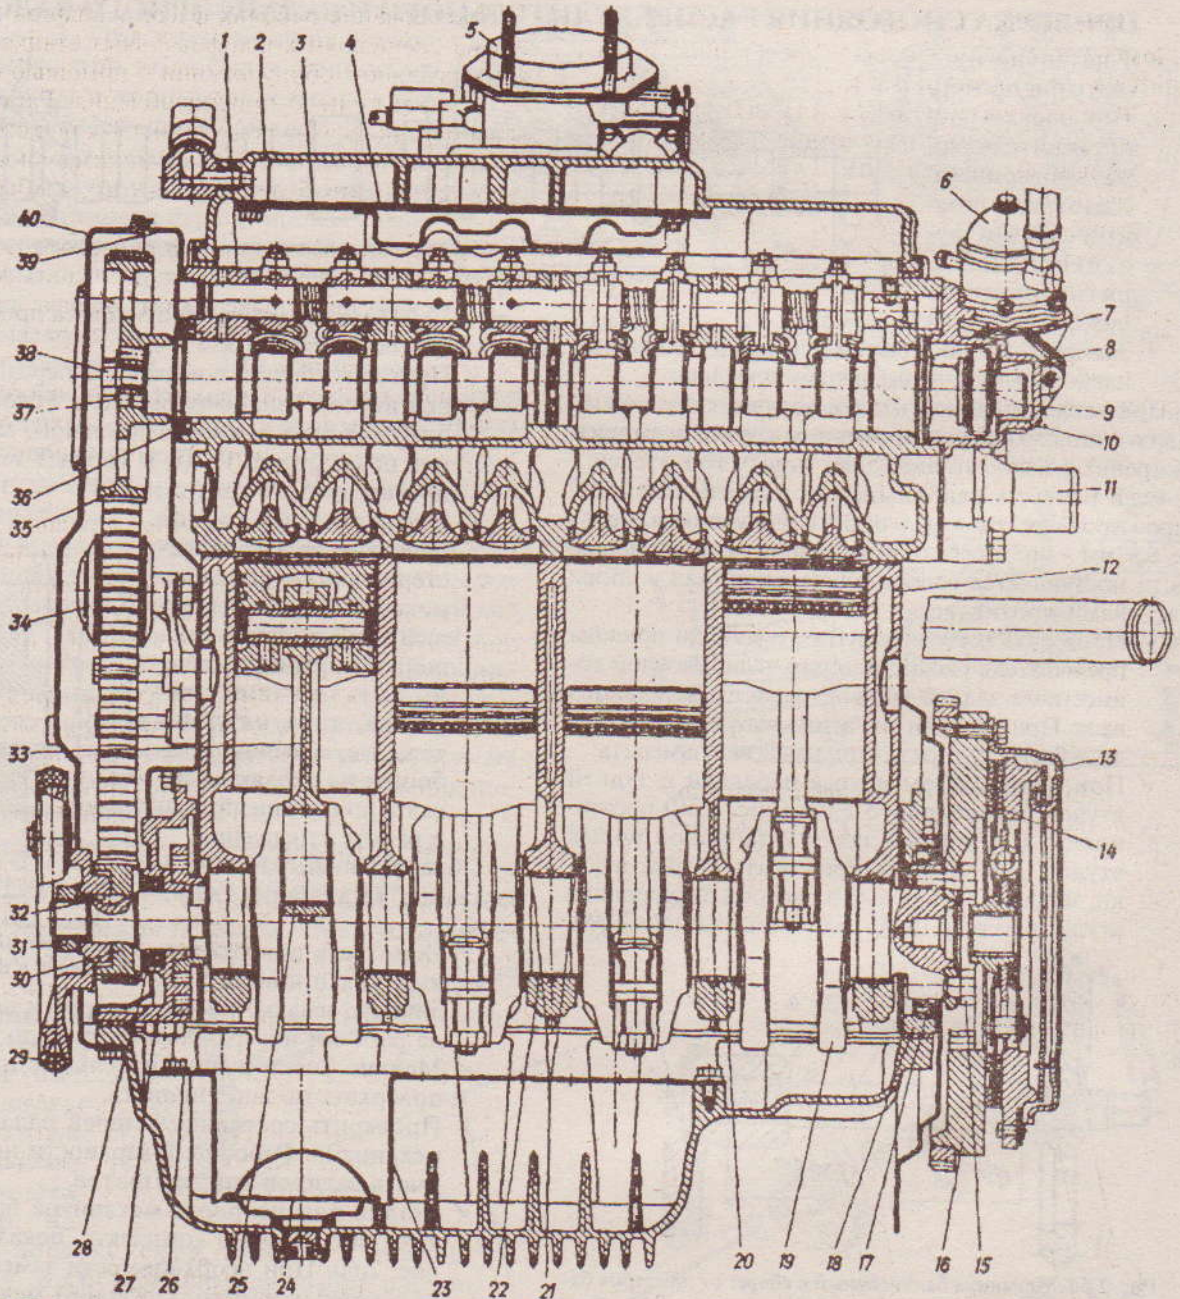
Продольный разрез двигателя: 1 - головка цилиндров; 2 - крышка головки цилиндров; 3, 4 - прокладка и крышка маслоотделителя; 5 - фланец карбюратора для крепления воздушного фильтра; 6 - бензиновый насос; 7 - вал распределительный; 8 - ведущая шестерня привода датчика распределителя; 9 - кулачок привода бензинового насоса; 10 - корпус привода датчика-распределителя и бензинового насоса; 11 - отводящий патрубок; 12 - блок цилиндров; 13 - нажимной диск сцепления; 14 - диск сцепления ведомый; 15, 38 - болты; 16 - маховик; 17, 28, 36 - манжеты; 18 - держатель манжеты; 19 - коленчатый вал; 20 - вкладыши коренных подшипников коленчатого вала; 21 - упорные полукольца коренного подшипника коленчатого вала; 22 - вкладыш среднего коренного подшипника коленчатого вала; 23 - приемник масляного насоса; 24 - маслосливная пробка; 25 - вкладыш нижней головки шатуна; 26 - масляный картер; 27 - масляный насос; 29 - шкив привода генератора; 30 - ведущий шкив коленчатого вала; 31 - гайка; 32 - шпонка; 33 - шатун с поршнем, поршневыми кольцами и пальцем; 34 - натяжной ролик; 35 - шкив привода распределительного вала; 37 - стопорная шайба; 39, 40 - внутренний и наружный кожухи плоскос зубчатого ремня
